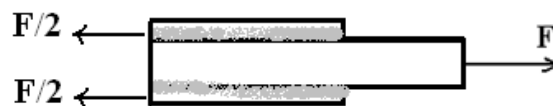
Soudure à clin ou à couvre joints cas latérale
